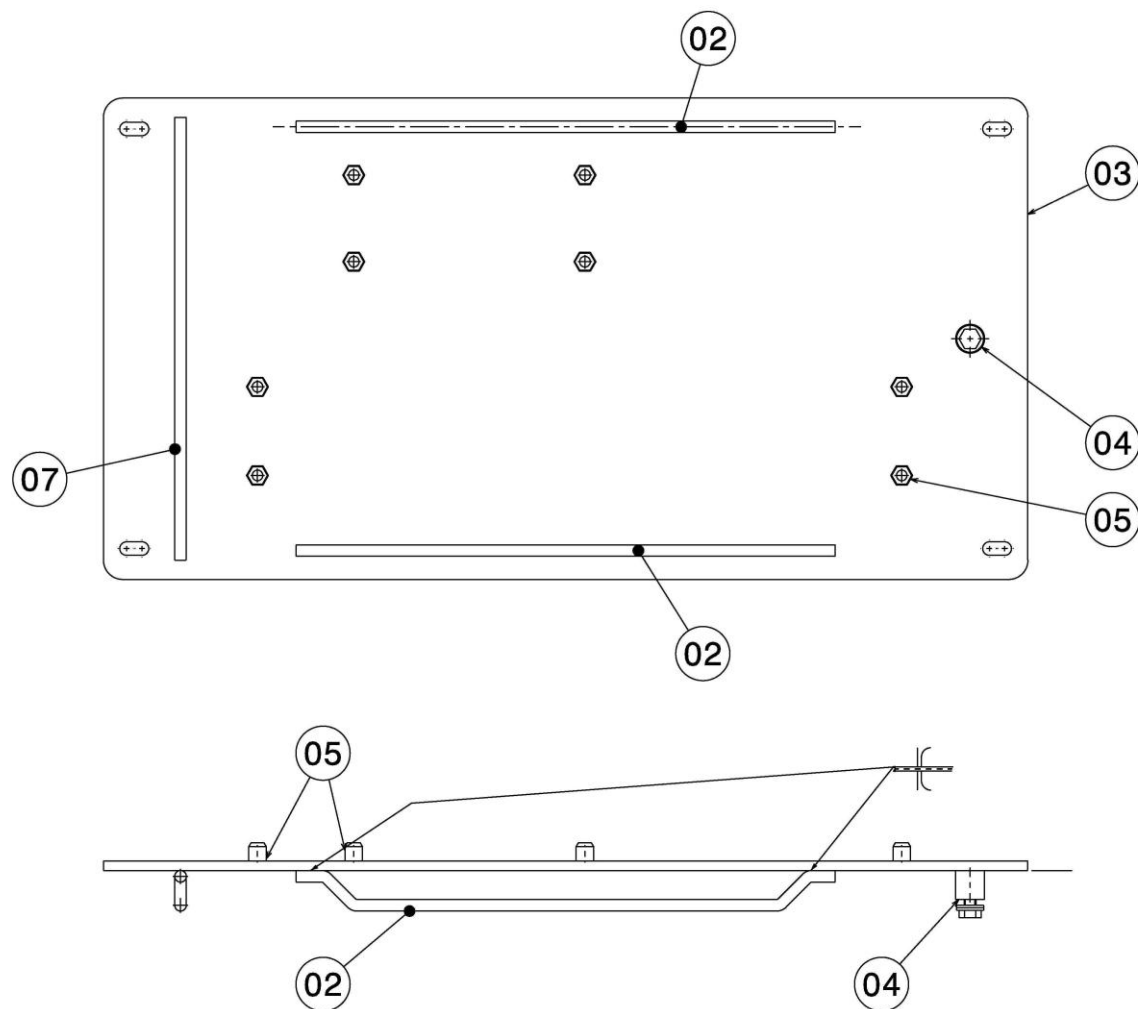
CONJUNTO SUPORTE DE CONTADORES.
